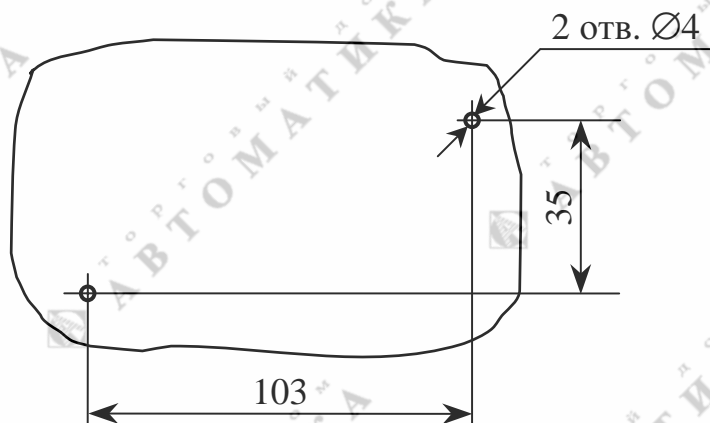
Разметка отверстий для крепления блока усилителя блока датчиков БД-902, БД-902А
